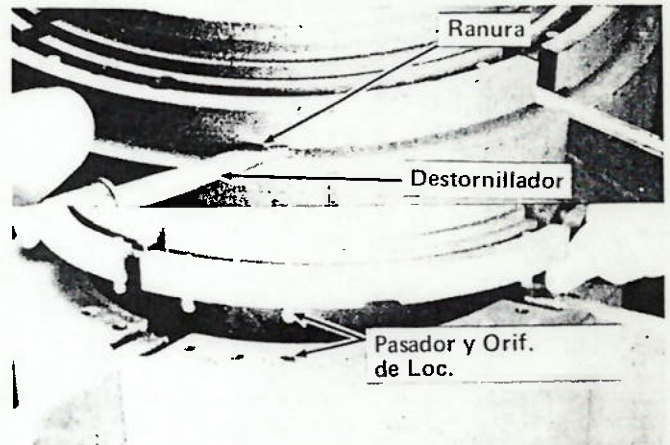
REMOCIÓN DE LA CUBIERTA DEL ROTOR.
